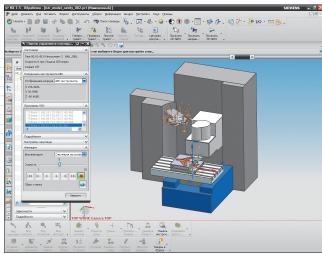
Общий вид симуляции обработки с использованием модели станка
